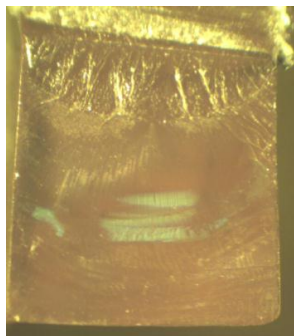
Superficie de fractura de una probeta grupo 1.
